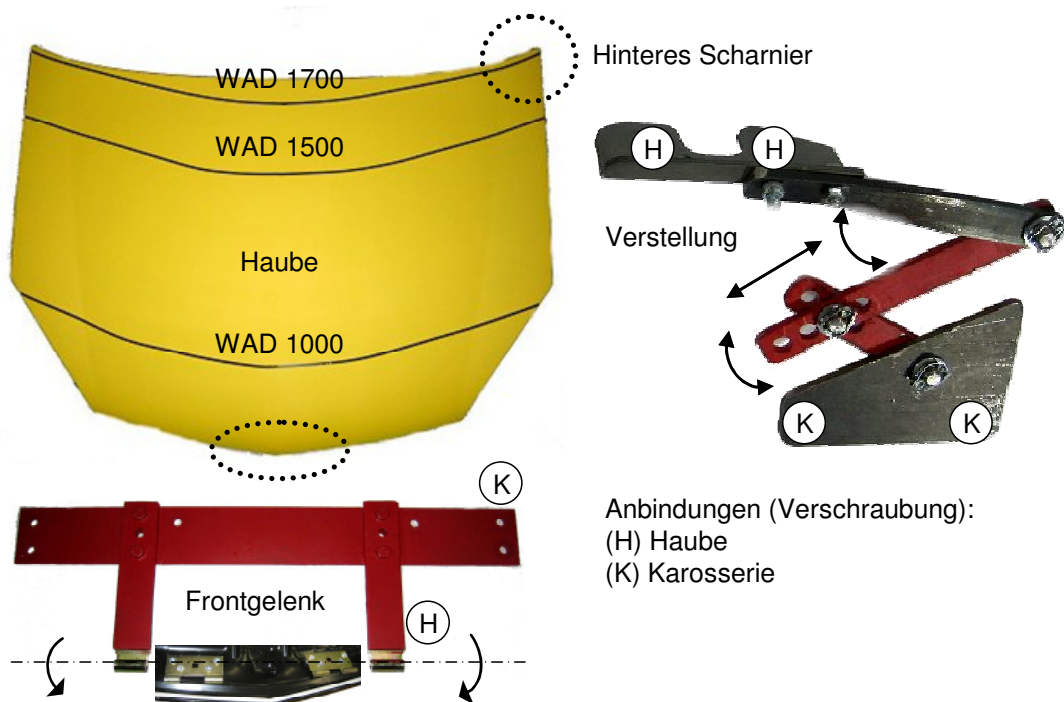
Komponenten der Motorhaube mit Anbindungen
